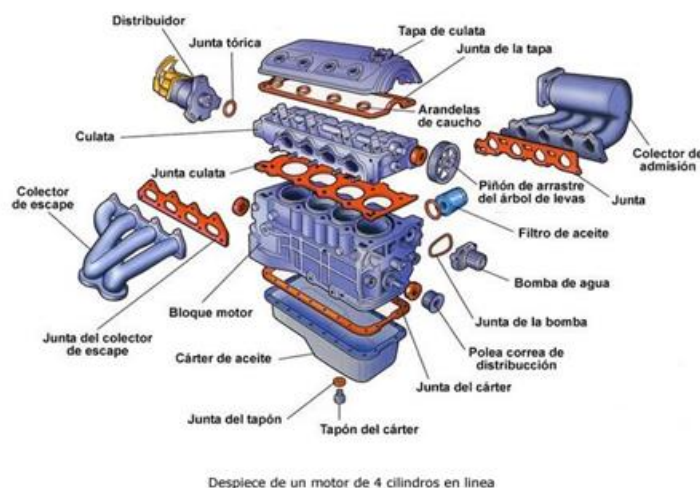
Explosionado de un MCIA. Fuente: MECANICA AUTOMOTRIZ [17]
